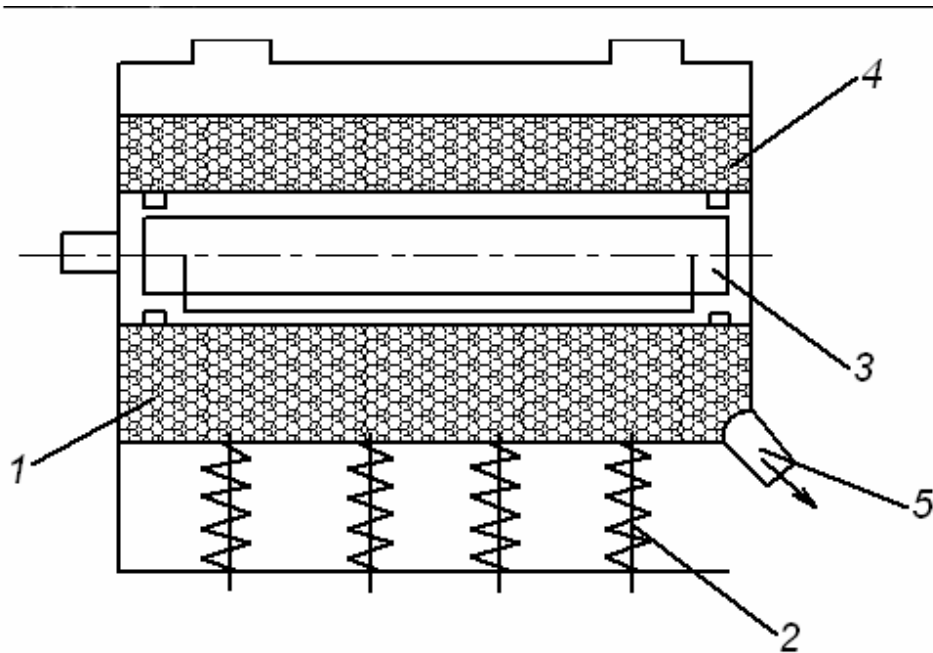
Вібраційний подрібнювач: 1 – корпус; 2 – пружини; 3 – вібруючий елемент; 4 – матеріал; 5 – вихідний патрубок
